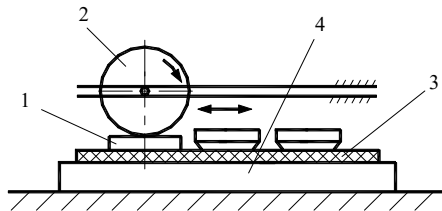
Схема пристрою для каткового способу розкroювання матеріалів
